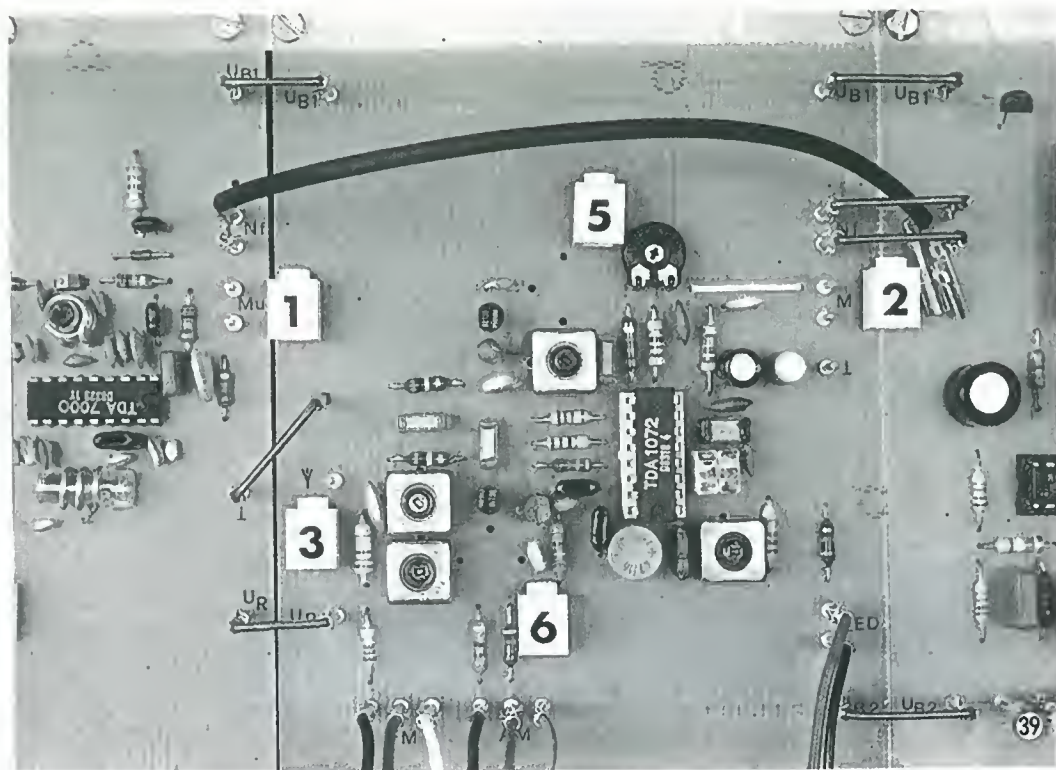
A sinistra della foto è visibile il ricevitore FM completo e collegato agli altri moduli.
